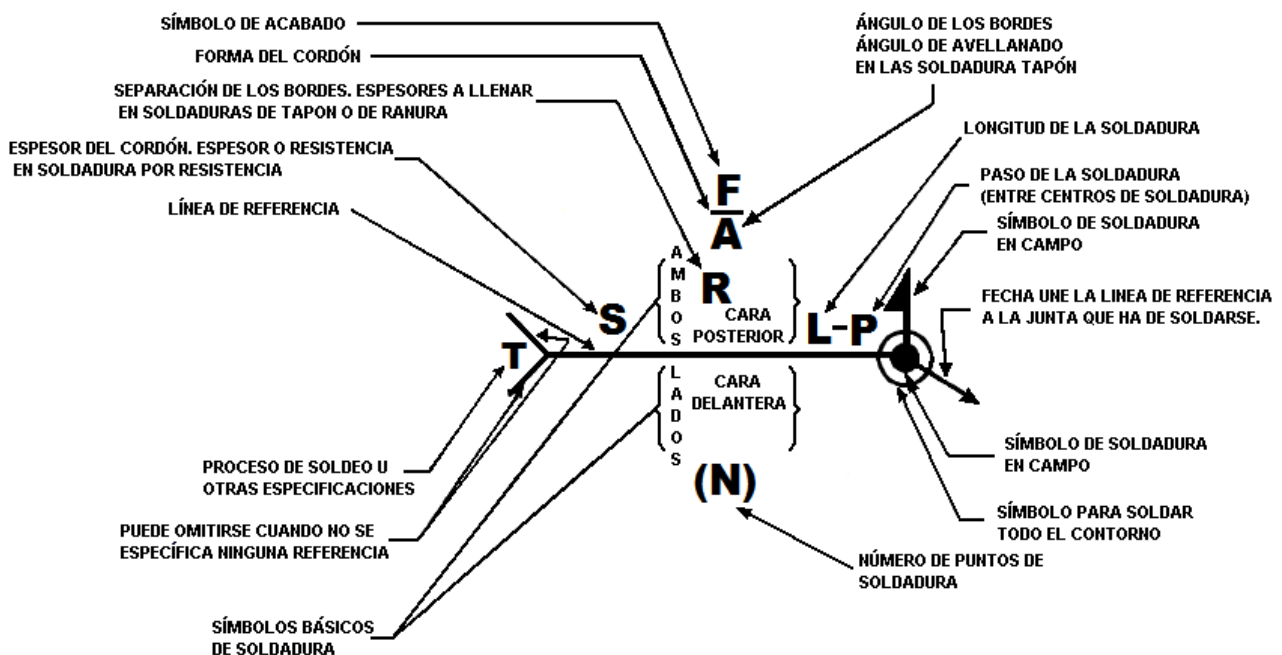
Modelo del símbolo de soldadura (3, 18, 27, 31)
